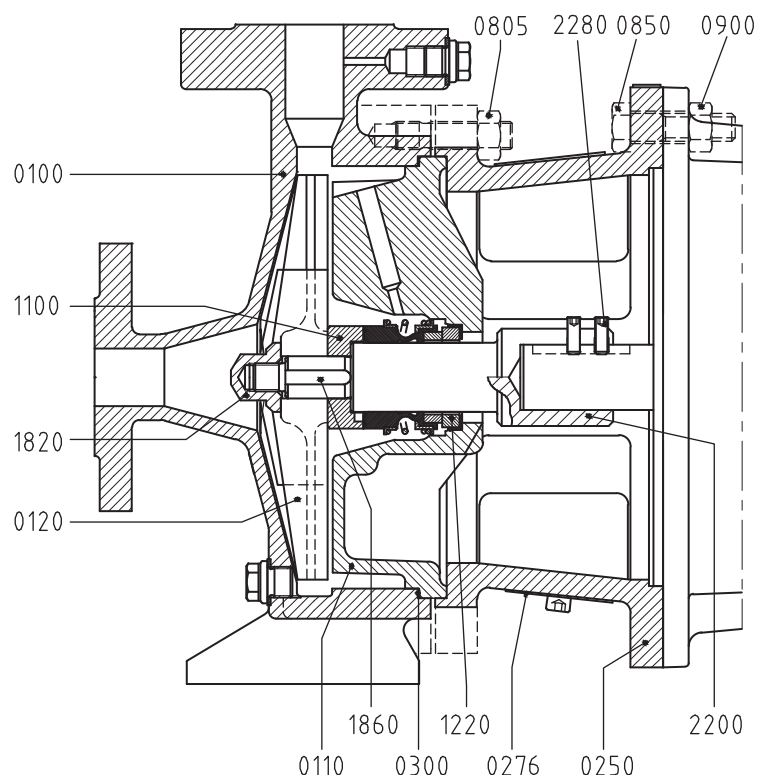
Сборка втулочного вала насоса размером 25 -...
